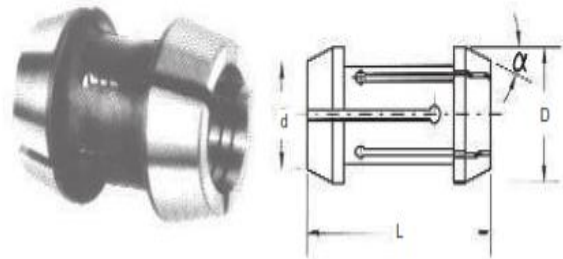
Les 2 types de modèle de pinces de serrage utilisées dans la machine.
